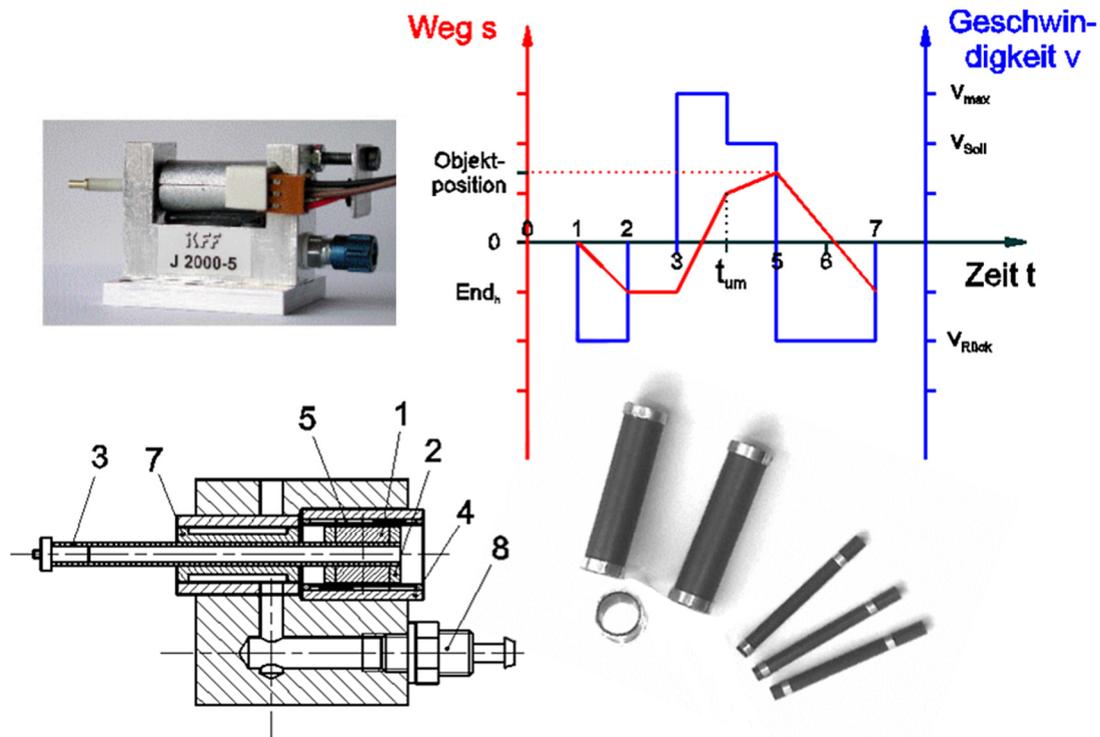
Linearantriebe für die Stoßjustierung feinwerk- und mikrotechnischer Baugruppen /25/
